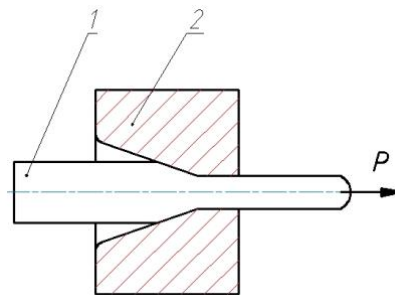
Схема волочіння: 1 – волока; 2 – заготовка.
